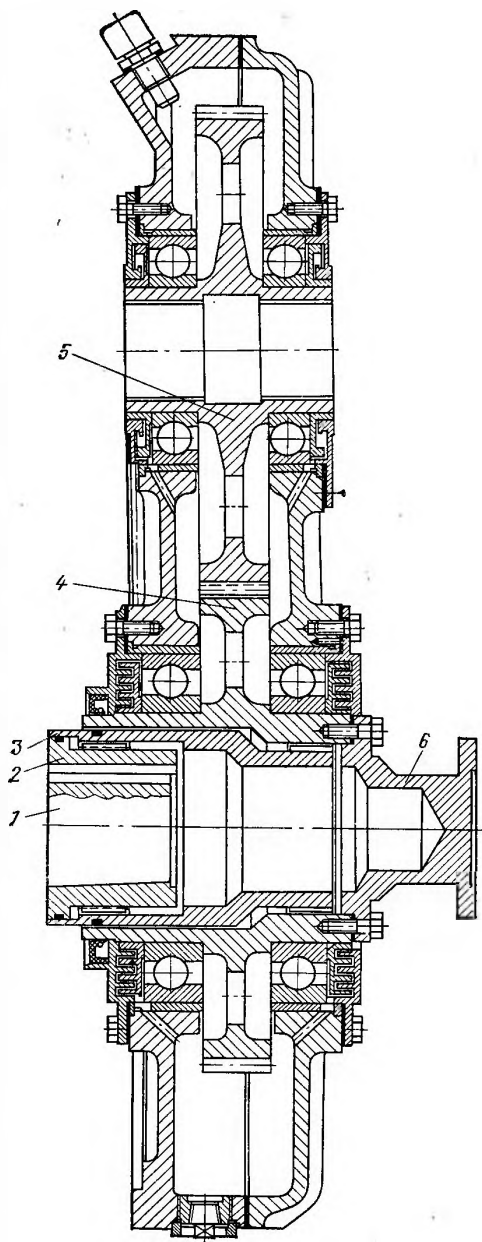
Раздаточный редуктор экскаватора ЭТР253
